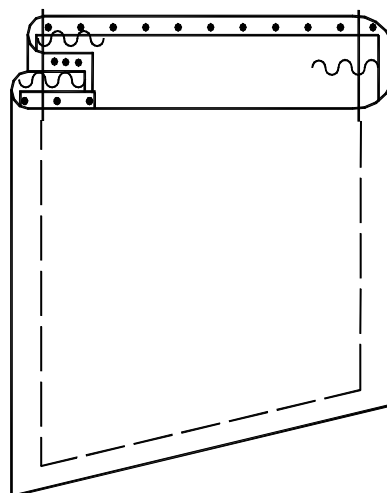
Монтажная схема конструкции цельновыкроенного съемного пояса накладным швом с двумя закрытыми срезами
